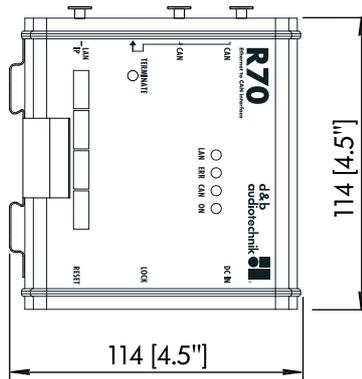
Wandmontage mit Abmessungen in mm [Zoll]
